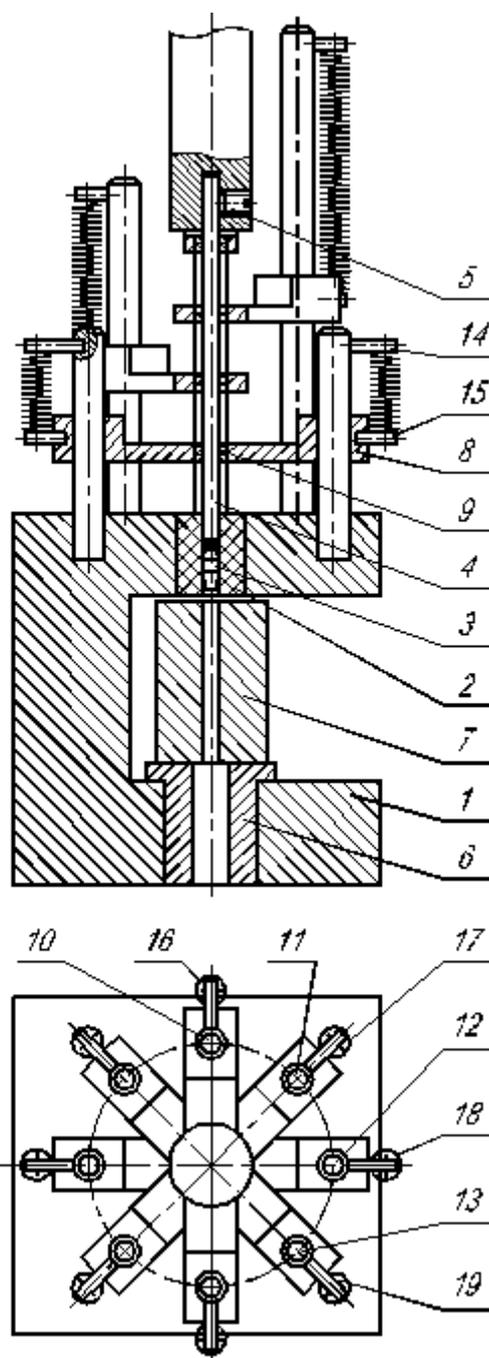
Устройство для дорнования глубоких отверстий малого диаметра с пластинчатыми направляющими для толкателя
